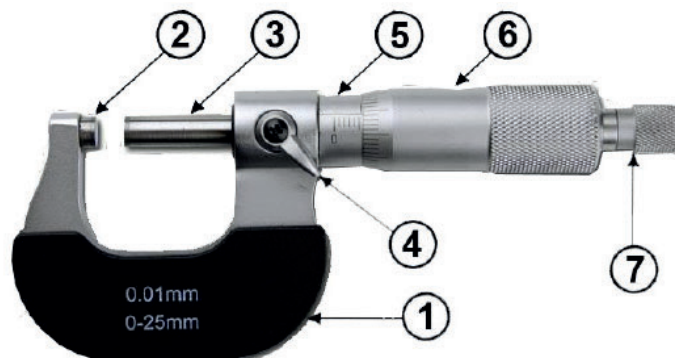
Будова мікрометра: 1 – скоба; 2 – п'ятка; 3 – мікрометричний гвинт; 4 – стопор; 5 – стебло; 6 – барабан; 7 – корпус тріскачки
